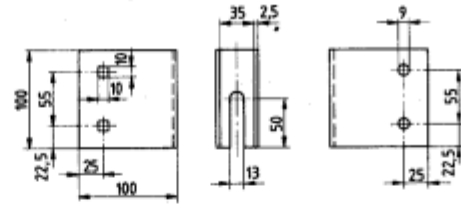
Formen, Maße und Ausführungen von Leitergerüstbauteilen aus Holz (Maße in mm)
